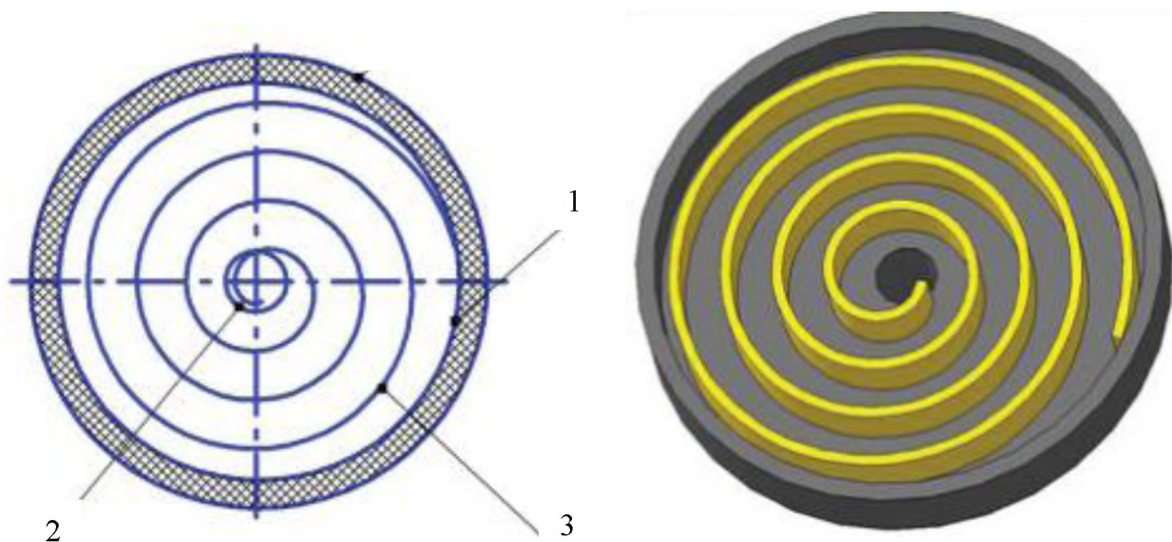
Схема сушильної камери: 1 – циліндричний кожух;
